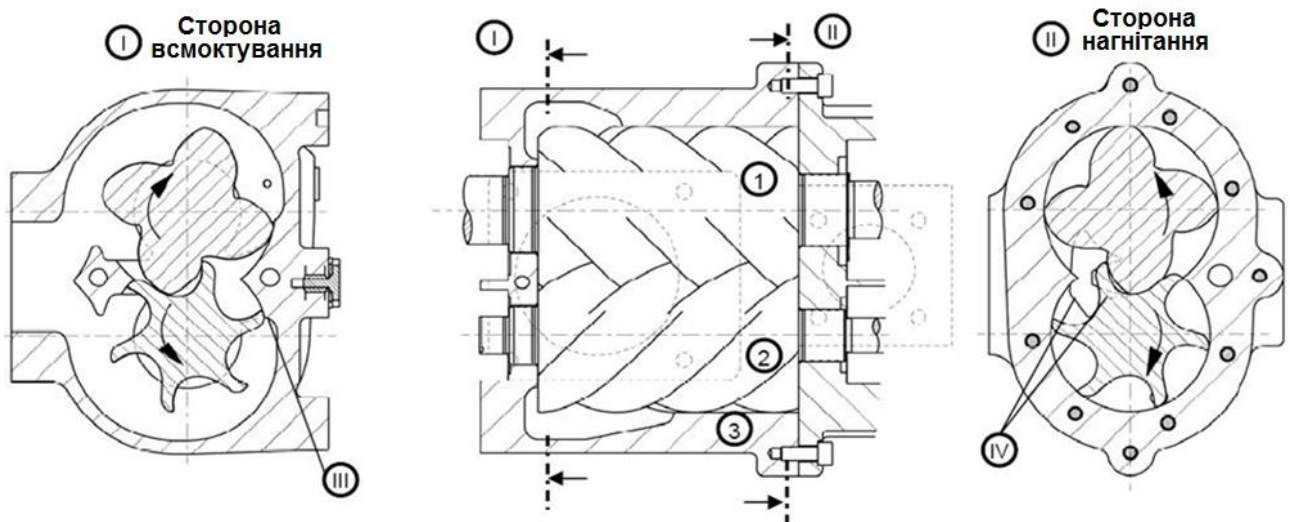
Схема роботи гвинтового блоку роторного компресора:
